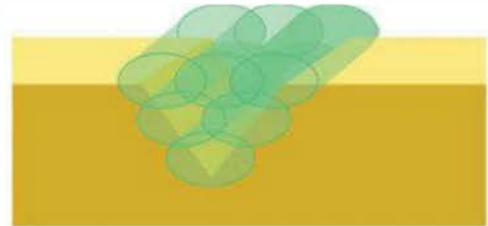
Soudage par friction des coutures, grâce à plusieurs couches
